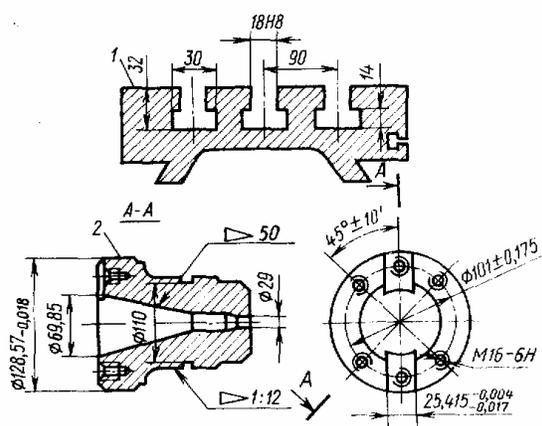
Установочные базы горизонтально-фрезерного станка 6Р82Г (1 – пазы стола; 2 – шпиндель)
